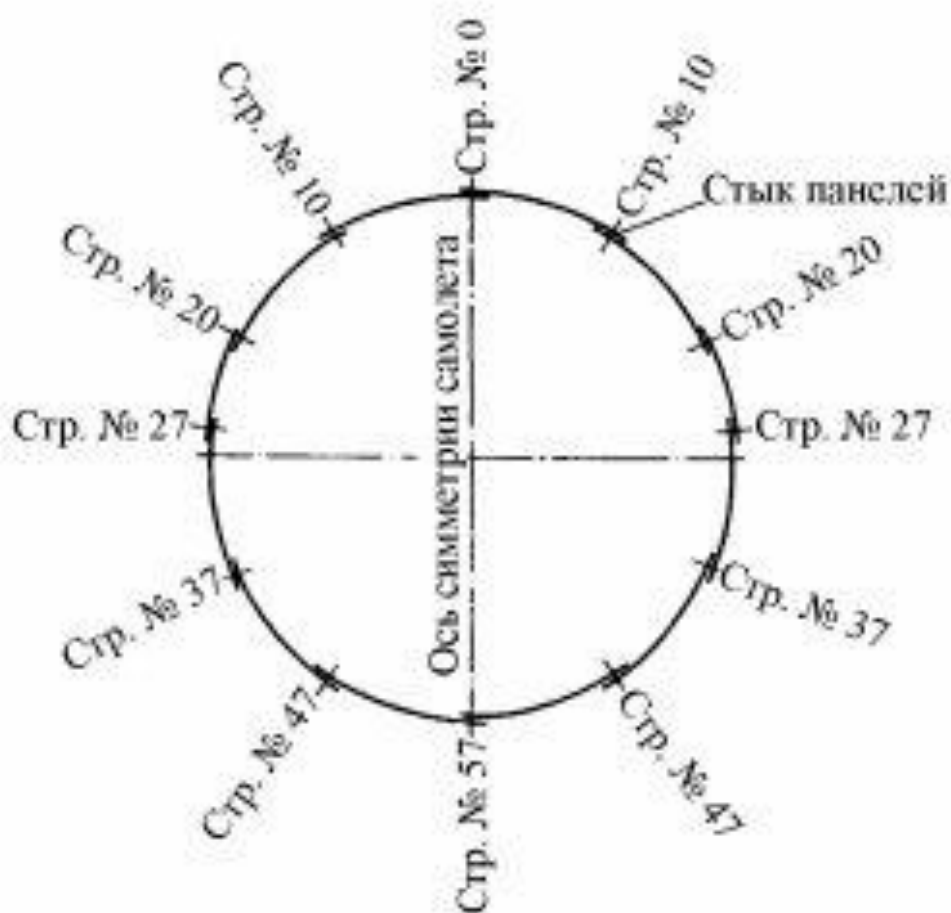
Поперечное сечение цилиндрической части фюзеляжа
